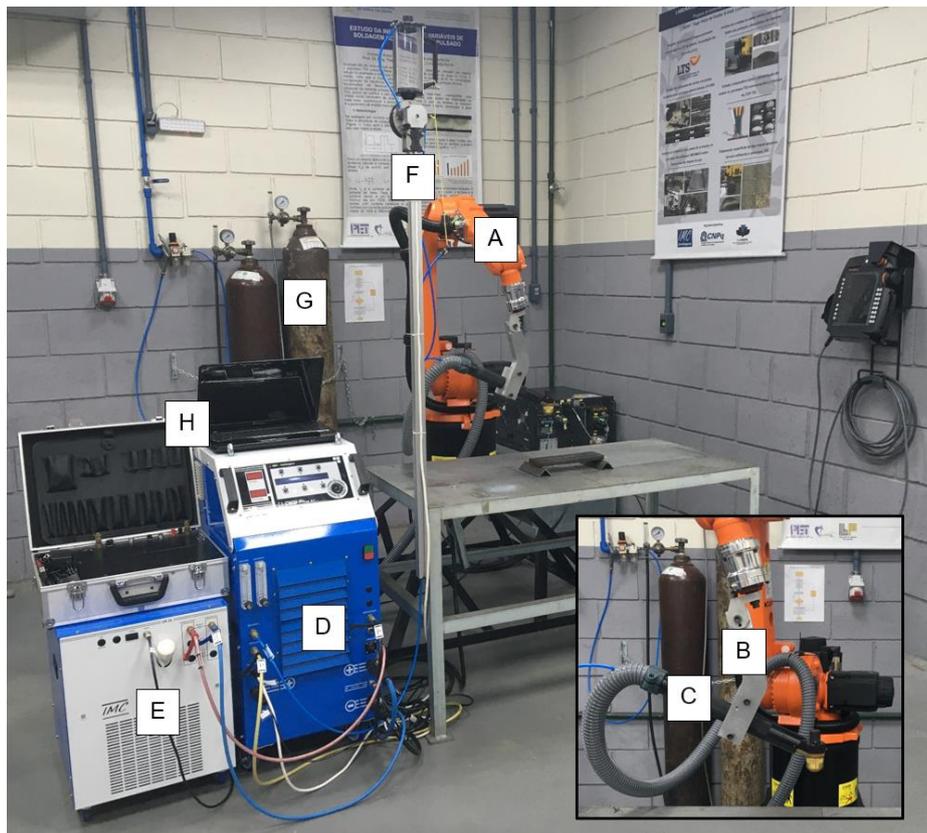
Bancada de ensaios composta por (A) robô de soldagem, (B) punho de fixação, (C) tocha de soldagem, (D) fonte de soldagem, (E) unidade de refrigeração, (F) alimentador de pó, (G) cilindros de gás e (H) sistema de aquisição SAP
